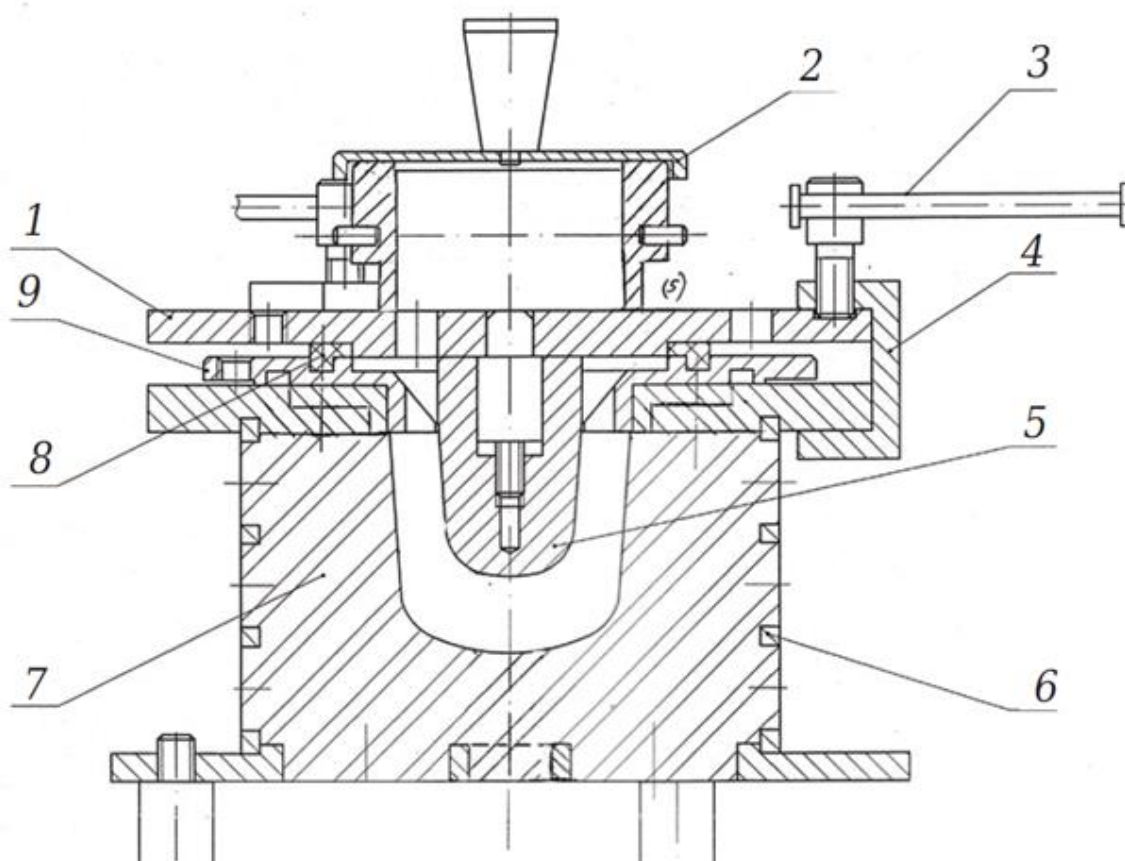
Схема формовочного комплекта в сборе: 1 – подвеска; 2 – крышка; 3 – винт; 4 – скоба; 5 – сердечник; 6 – форма; 7 – гипс; 8, 9 – кольцо [12]
